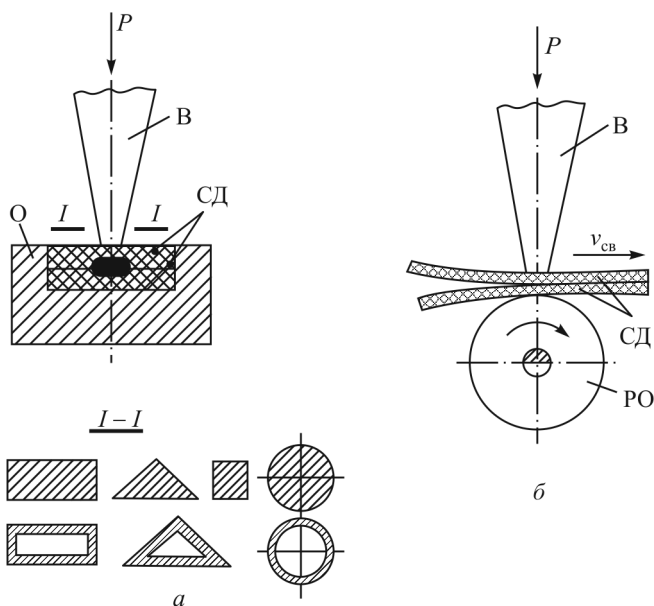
Контактная ультразвуковая сварка: *а* – прессовая; *б* – шовная: В – волновод, СД – свариваемые детали, РО – роликовая опора, О – опора;  $P$  – давление,  $v_{св}$  – скорость сварки
